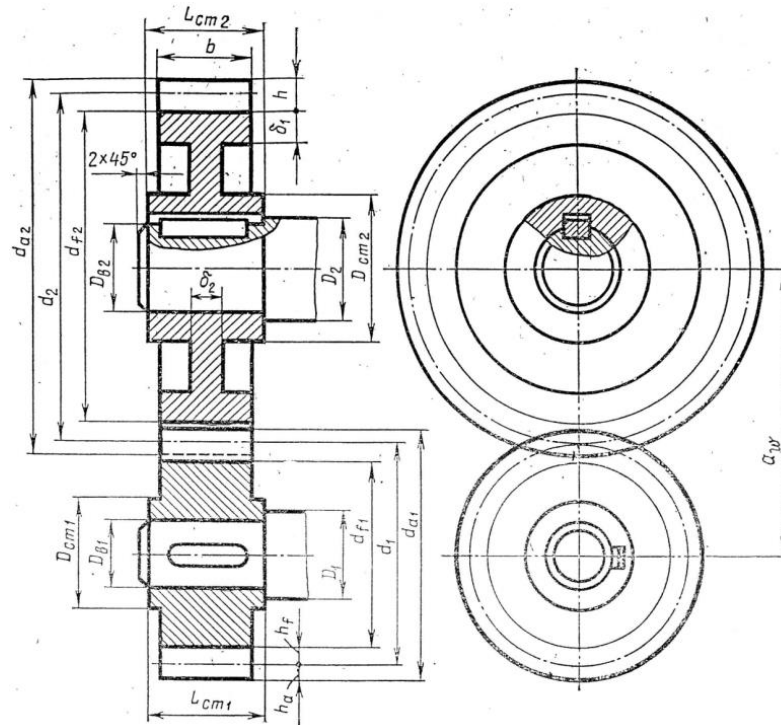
Зубчасте зачеплення циліндричної передачі
